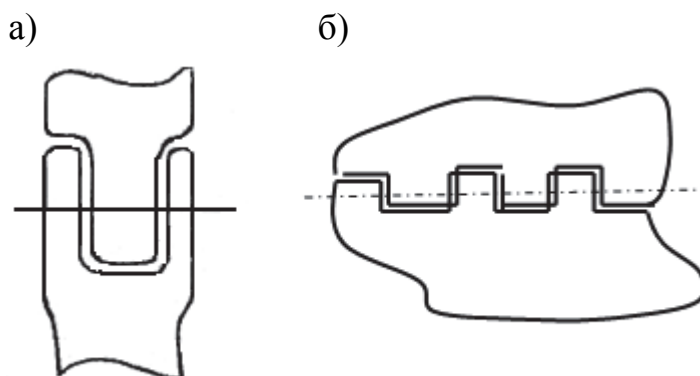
Стыки: а – «ухо-вилка»; б – «гребенка»
